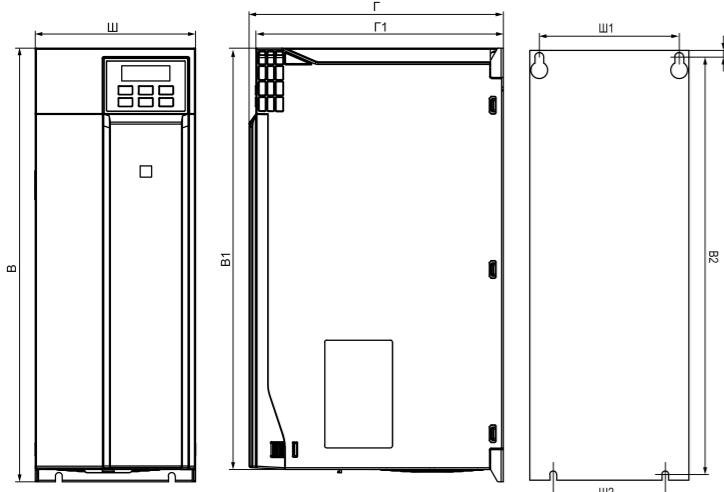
Габаритные размеры прибора в корпусе типоразмера 3
